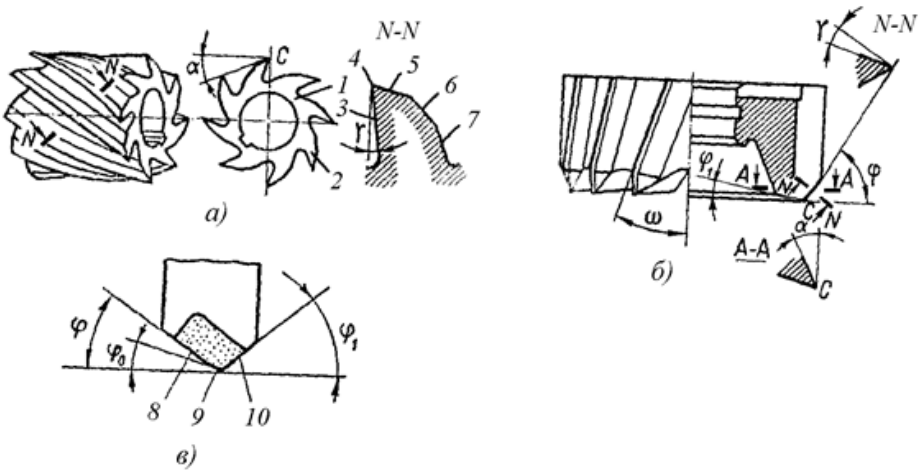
Геометричні параметри ріжучої частини циліндричної і торцевої фрези
